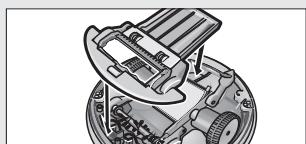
Montaje de la tapa del depósito acumulador de suciedad
